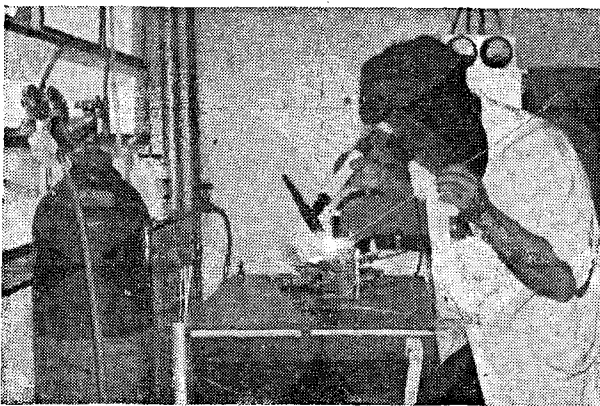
Solda do conjunto de moldura pelo processo de arco elétrico sob atmosfera de argônio.
